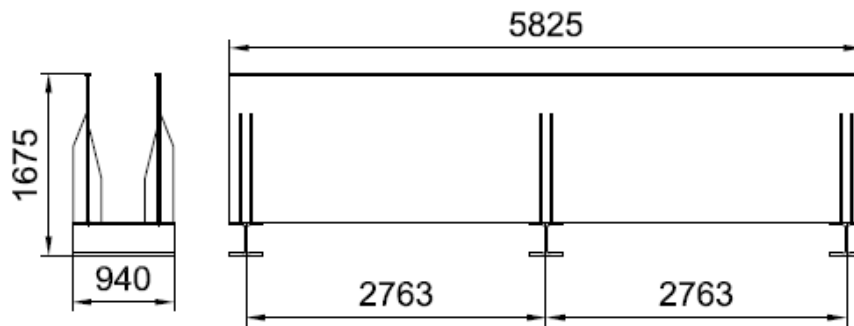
BG3; Position 1, Vorderansicht und Seitenansicht
